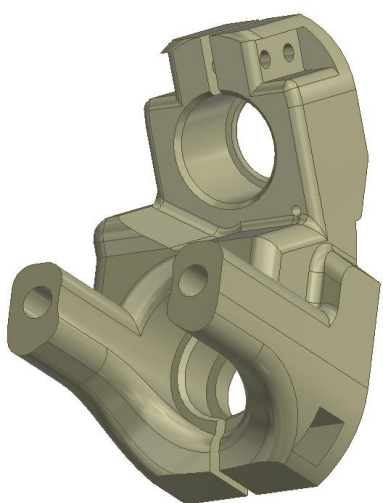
Zadní nápravová tyč - díra pro připojení zadní spojovací součásti
